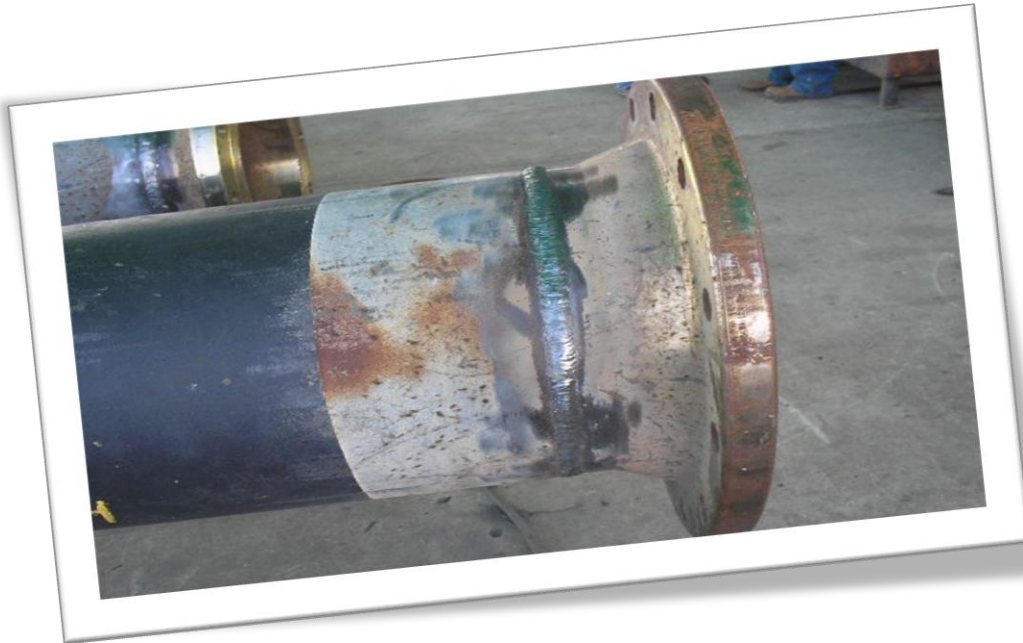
Foto que muestra Brida soldada a un Tubular
